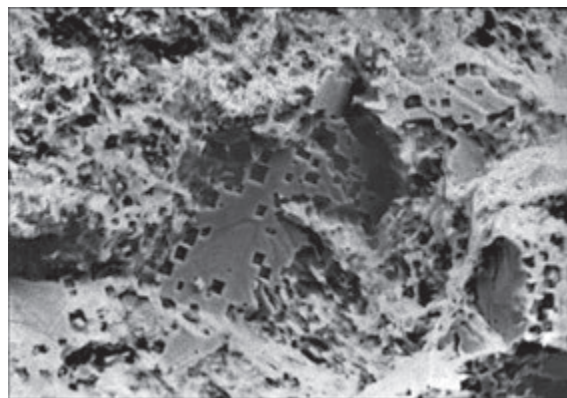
Пори у зварному шві, які виникли за рахунок неякісного зварювання
